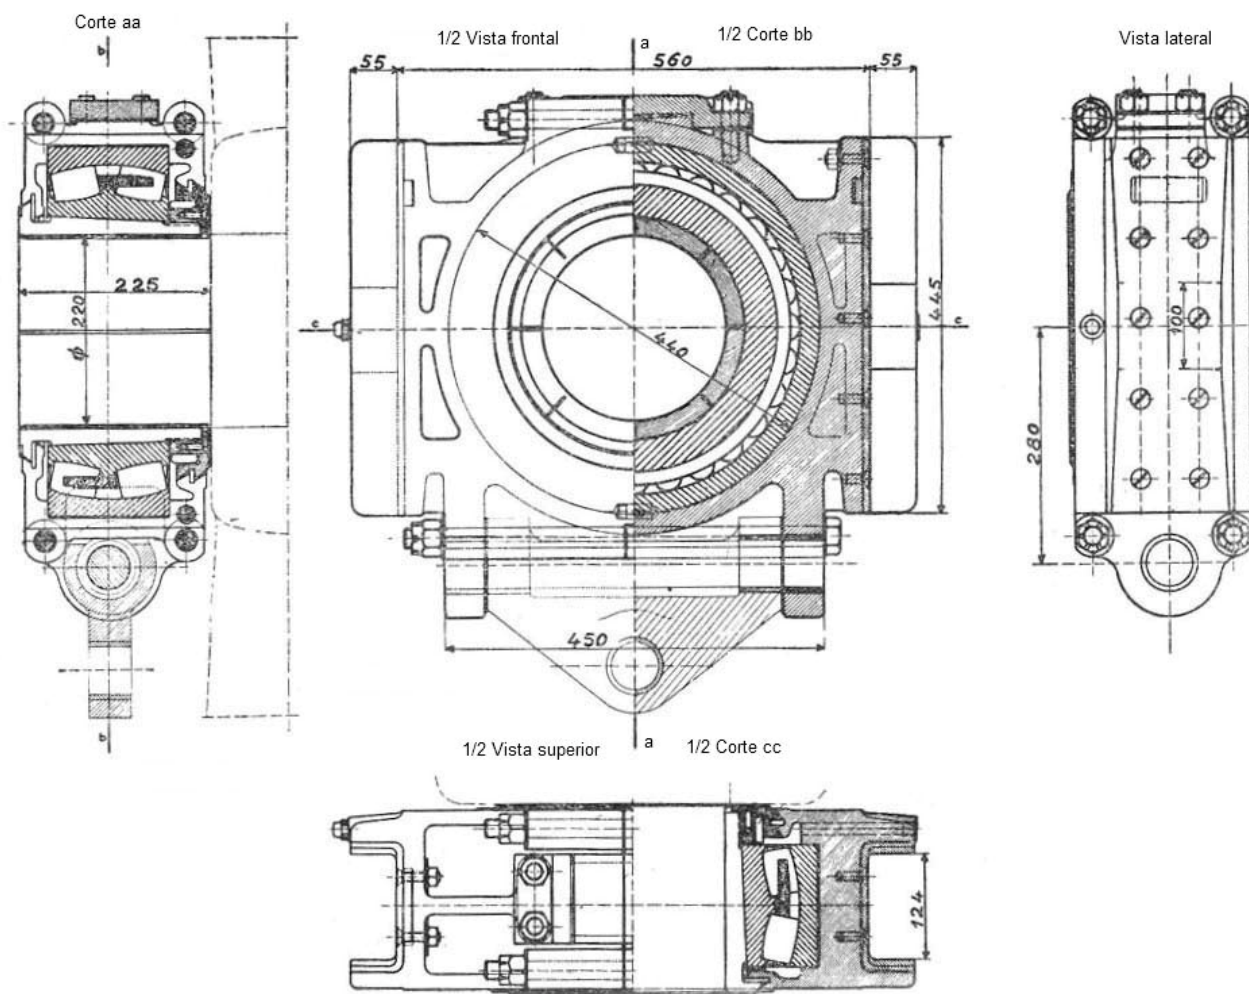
Caja a rodillos SKF del eje BP de las locomotoras 241 P del Sureste.
